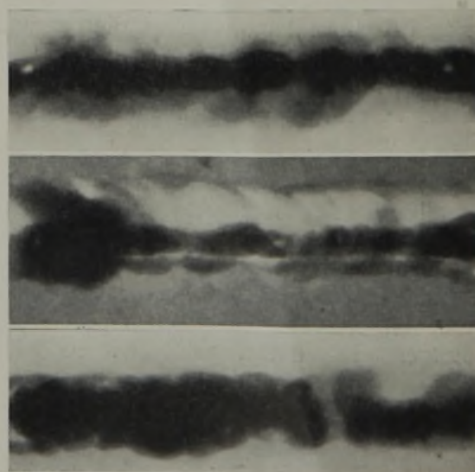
Proben schlechter Autogenschweißungen.
